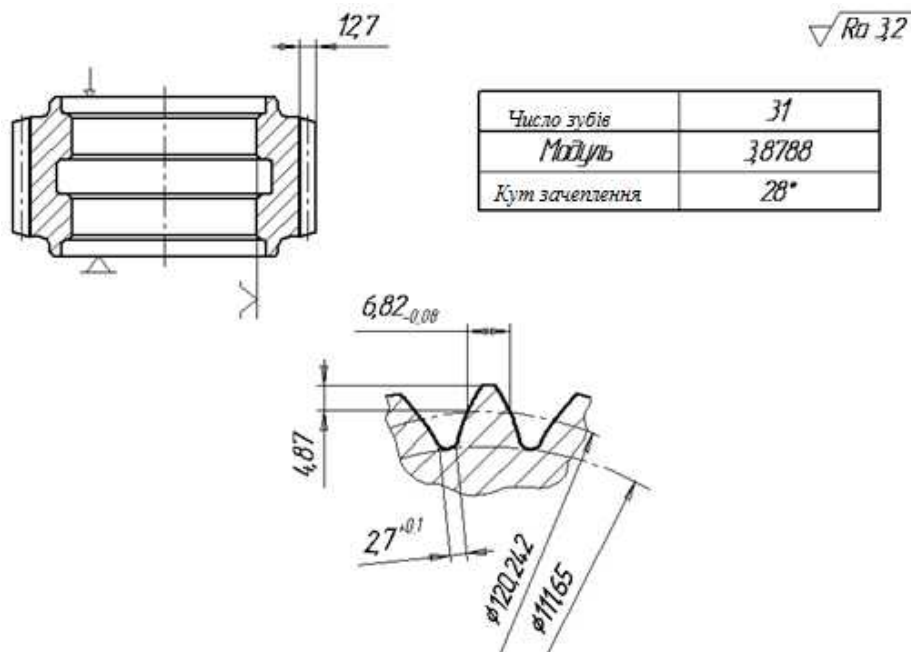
Операційний ескіз зубофрезерної операції 055
